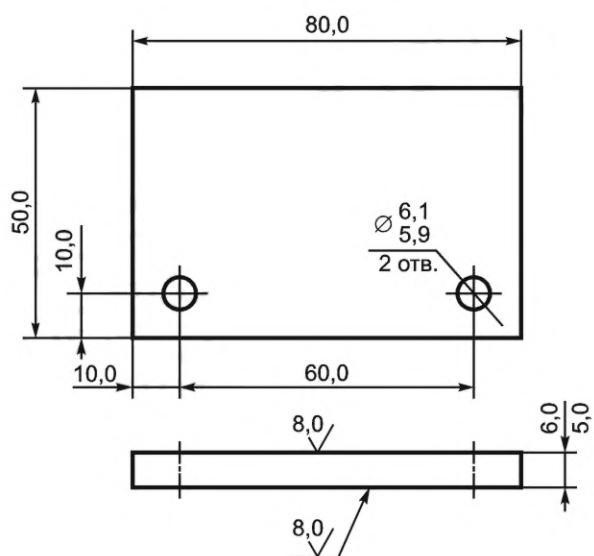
Прижимная пластина с дополнительно нарезанной резьбой
